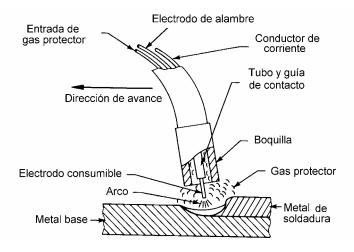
Detalle del arco de soldadura en el proceso GMAW.
